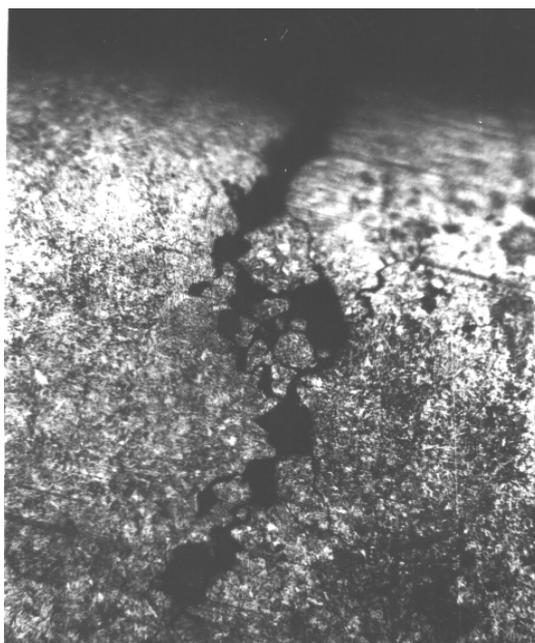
Поверхностная микротрещина на зубчатом колесе коробки передач трактора ТДТ-55А
